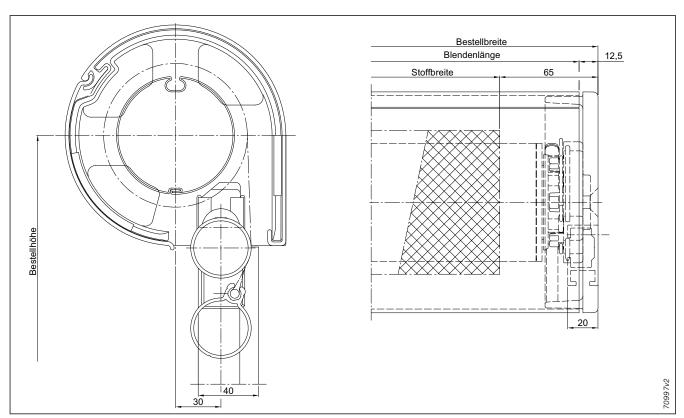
Markisolette 101, mit Rundblende Typ 8.3
